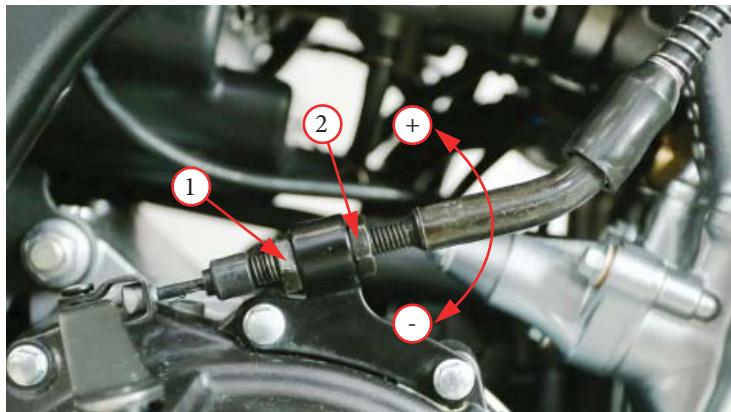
Регулировка сцепления на двигателе: двигателе:
